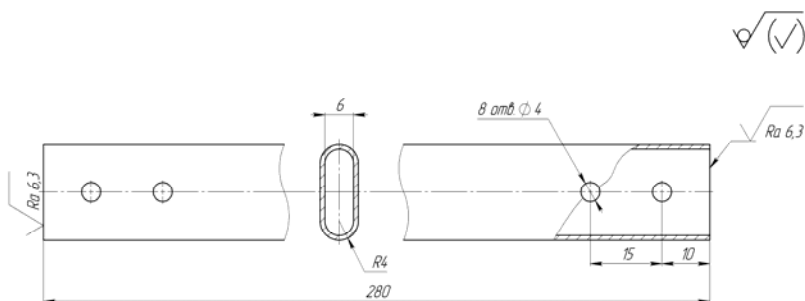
Кресленик деталі, що виготовлена з фасонної труби
